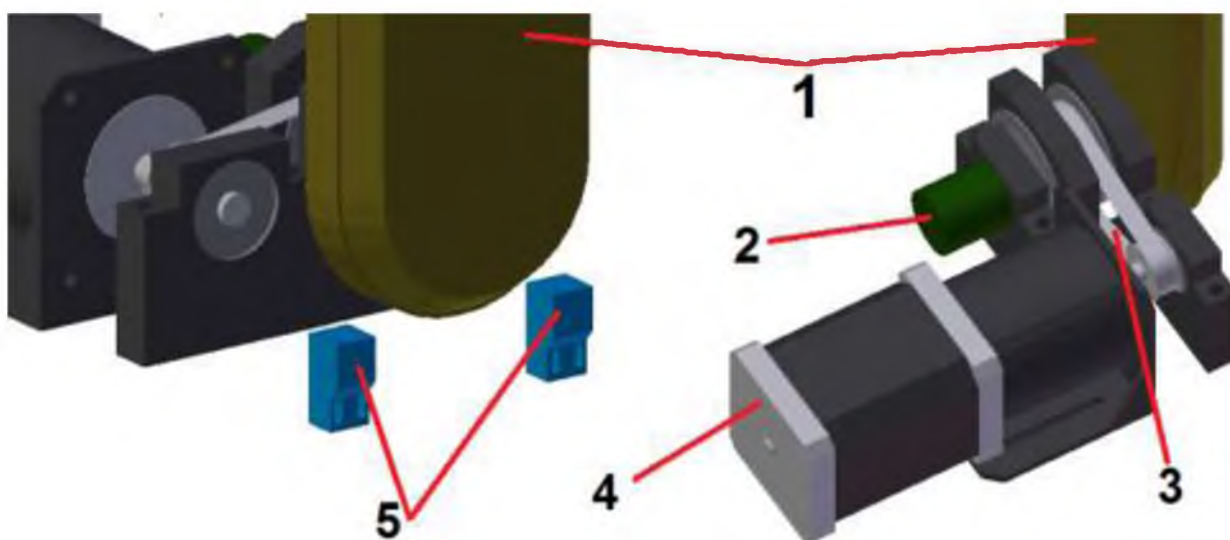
Схема типового узла: 1 – плечо манипулятора; 2 – энкодер; 3 – ременная передача; 4 – двигатель с редуктором; 5 – концевые выключатели.
